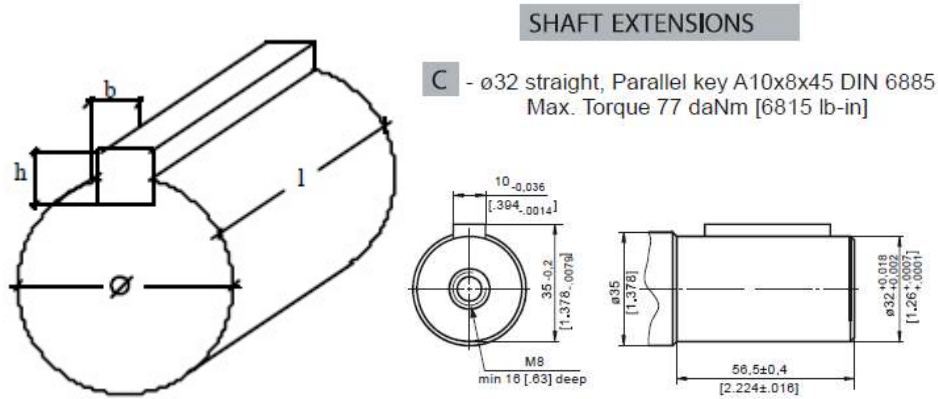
Dimensiones de la chaveta y el eje del motor hidráulico.
